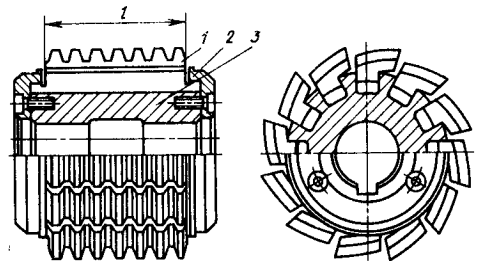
Сборная червячная фреза с поворотными вставными рейками
